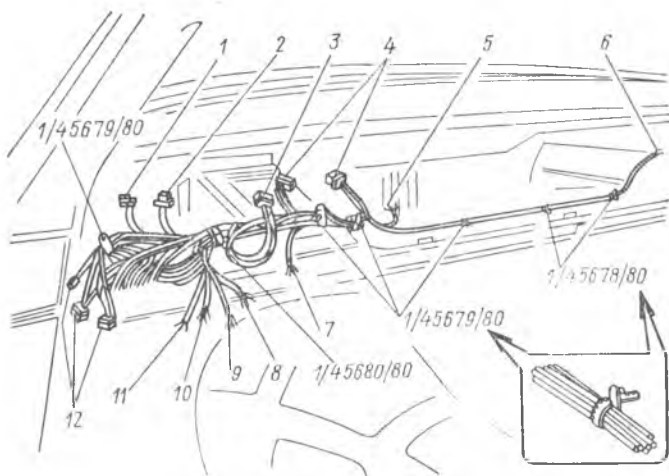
Укладка и крепление переднего пучка проводов на поперечине панели приборов
